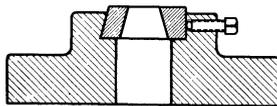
Befestigung der Schnittplatte durch einfache Schräge und Druckschraube.
